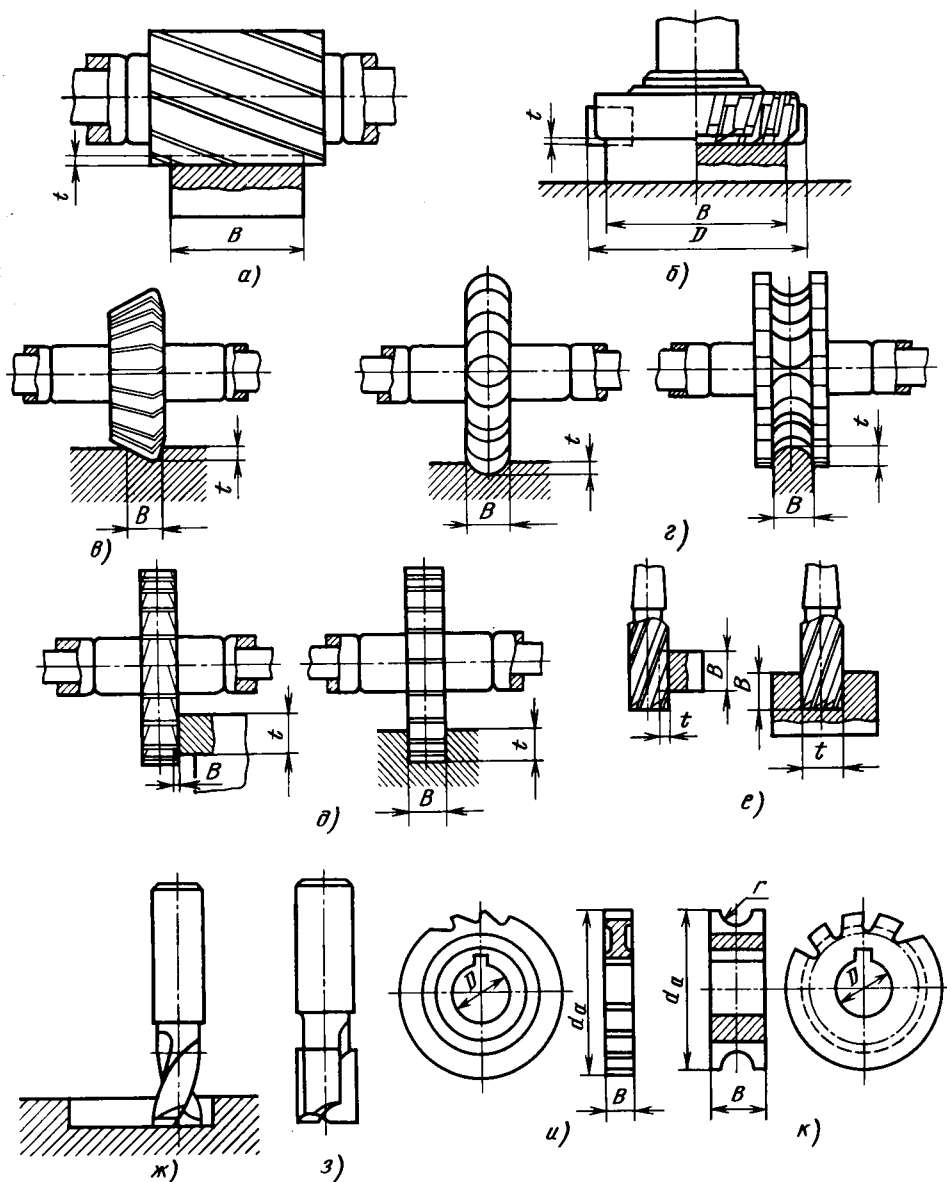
Типы фрез и обрабатываемых поверхностей
